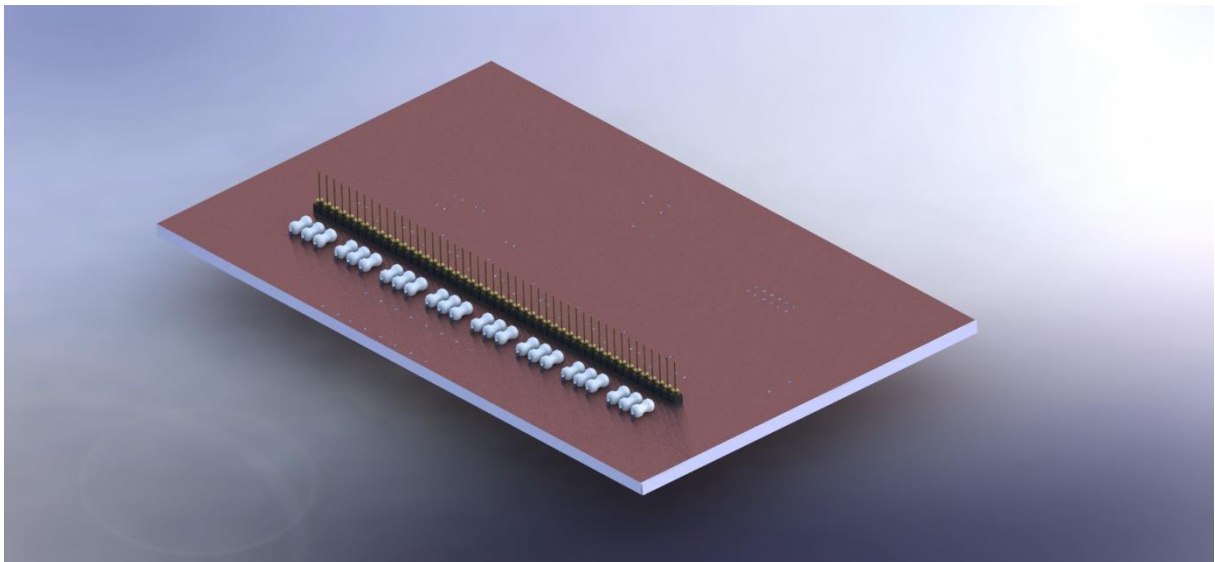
PCB entradas: Elementos acondicionamiento de señal en vista isométrica.
